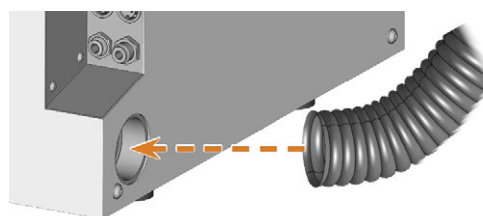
INSÉRER LE TUYAU D'ASPIRATION DANS LA MACHINE
